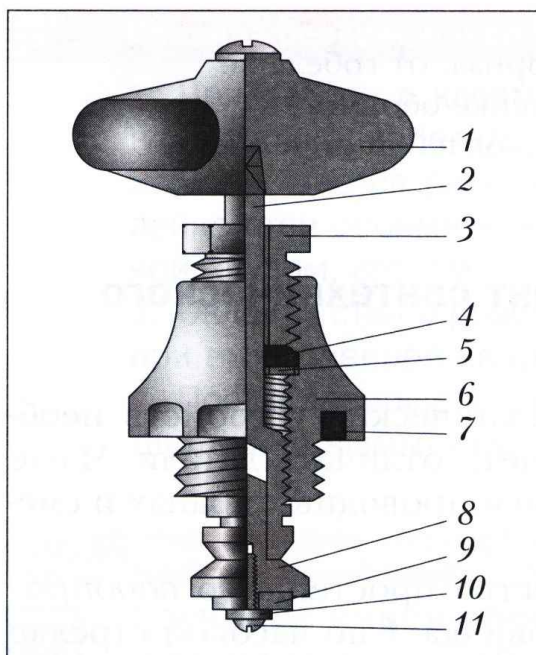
Устройство вентиляльной головки: 1 – маховичок; 2 – шпindelь; 3 – гайка; 4 – сальник; 5 – шайба; 6 – корпус; 7 – прокладка; 8 – клапан; 9 – прокладка; 10 – шайба; 11 – винт
